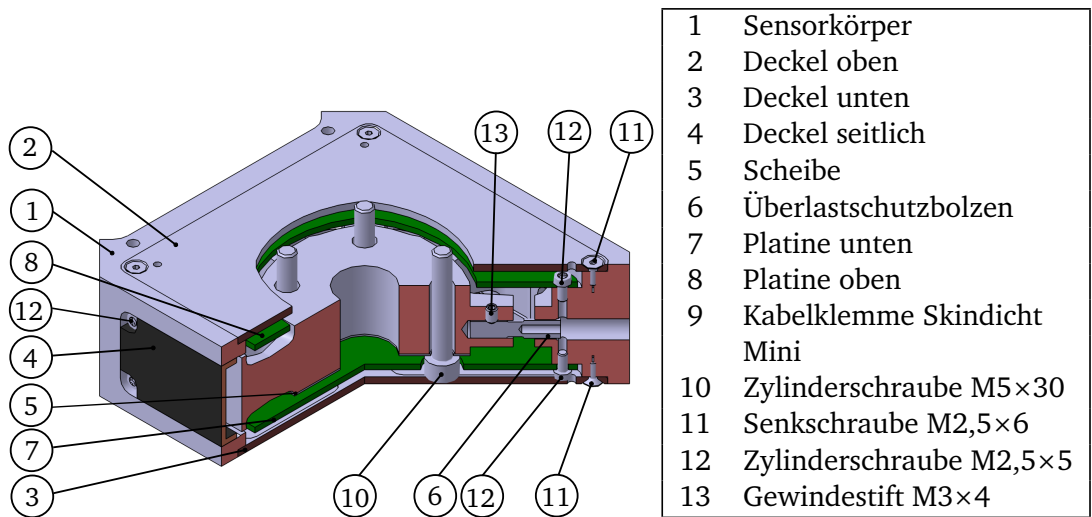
Zusammenbau und Explosionszeichnung des Kraftsensors.
